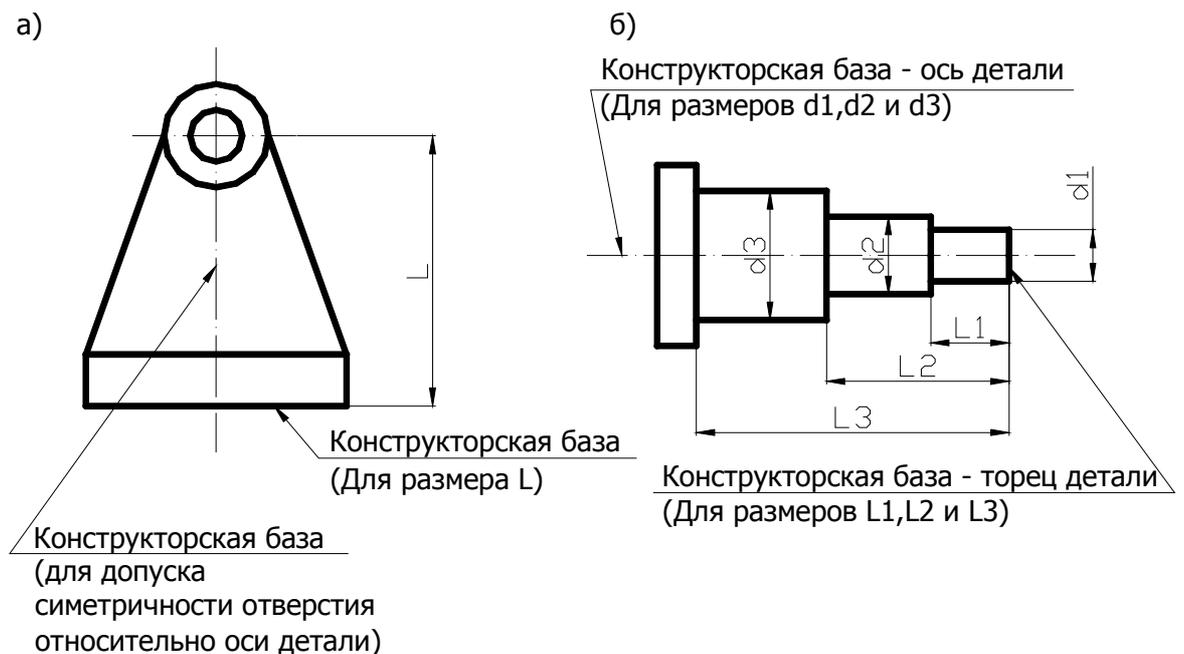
Примеры определения положения конструкторских баз для обрабатываемого сквозного отверстия (а) и ступенчатого вала (б).
